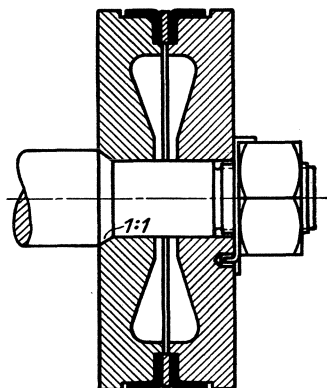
Geteilter Scheibenkolben für Wasserpumpen.
